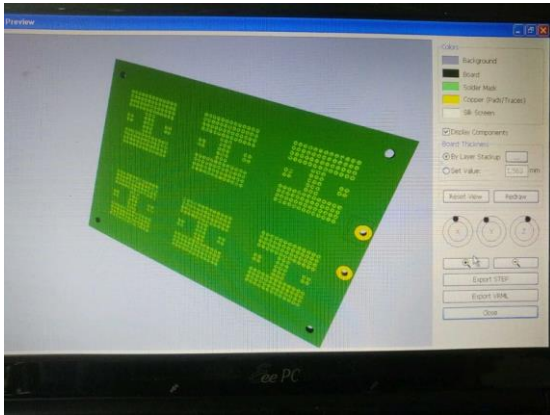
3D-Ansicht der PCB-Leiterplatte am Bildschirm
